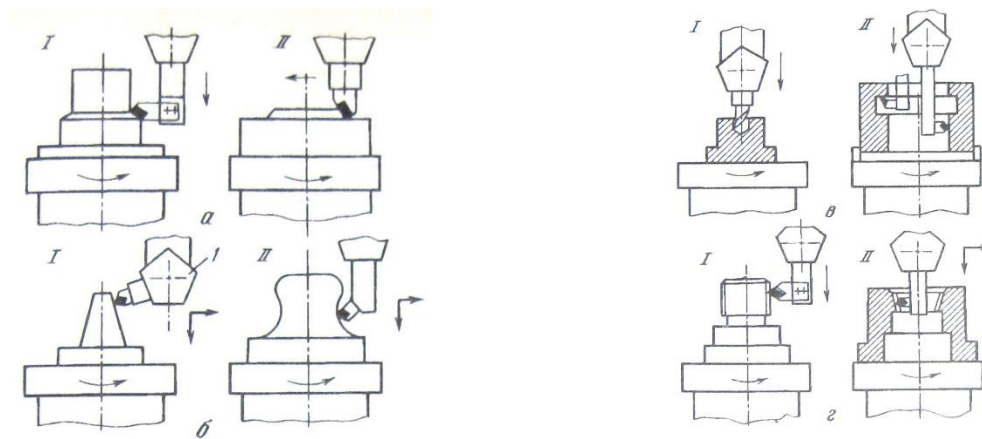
Типові схеми обробки на верстаті 1А563Ф4
